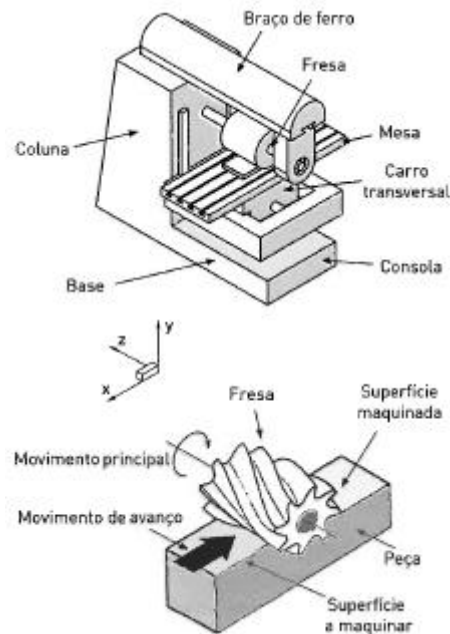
Fresagem cilíndrica numa fresadora horizontal [17].
